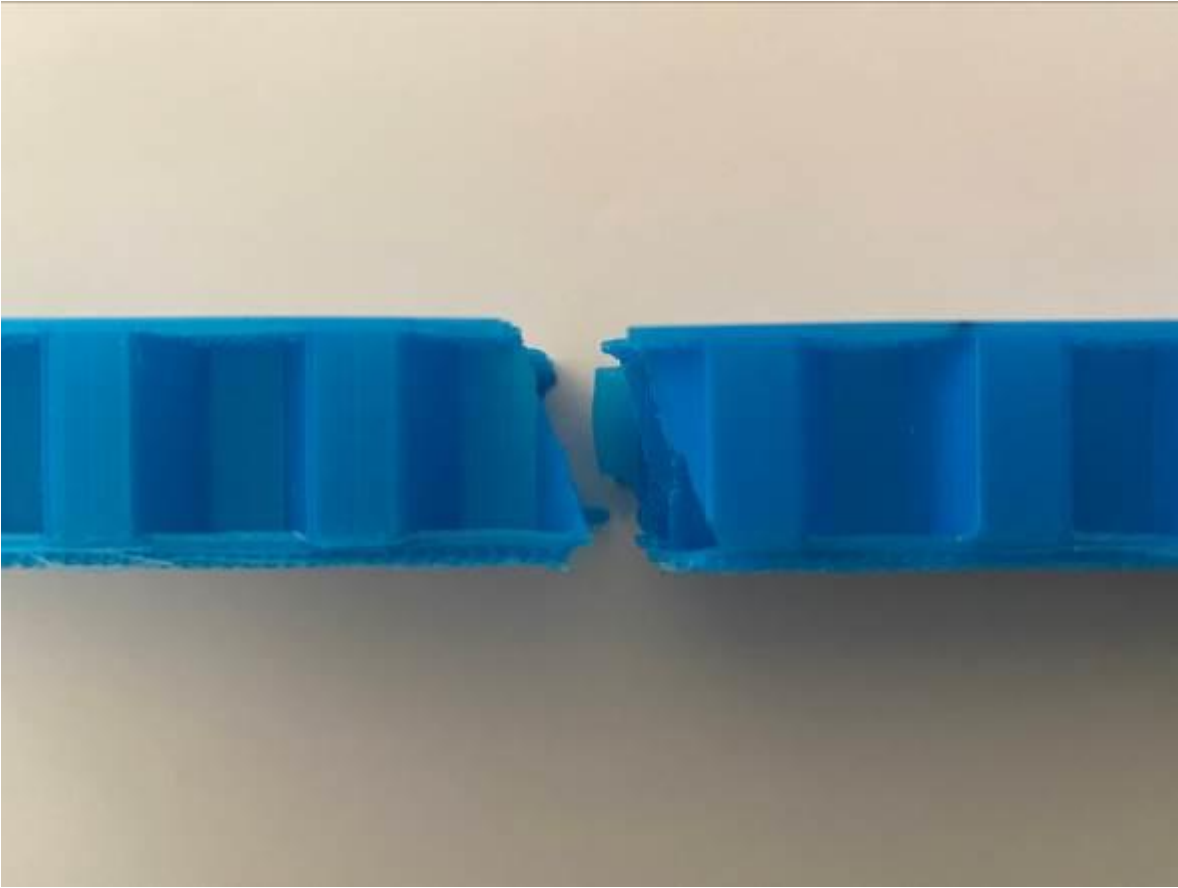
Espécimen 4 del lote de 3/8" fabricado completamente en PLA con tratamiento térmico, tipo de falla X-A-F.
